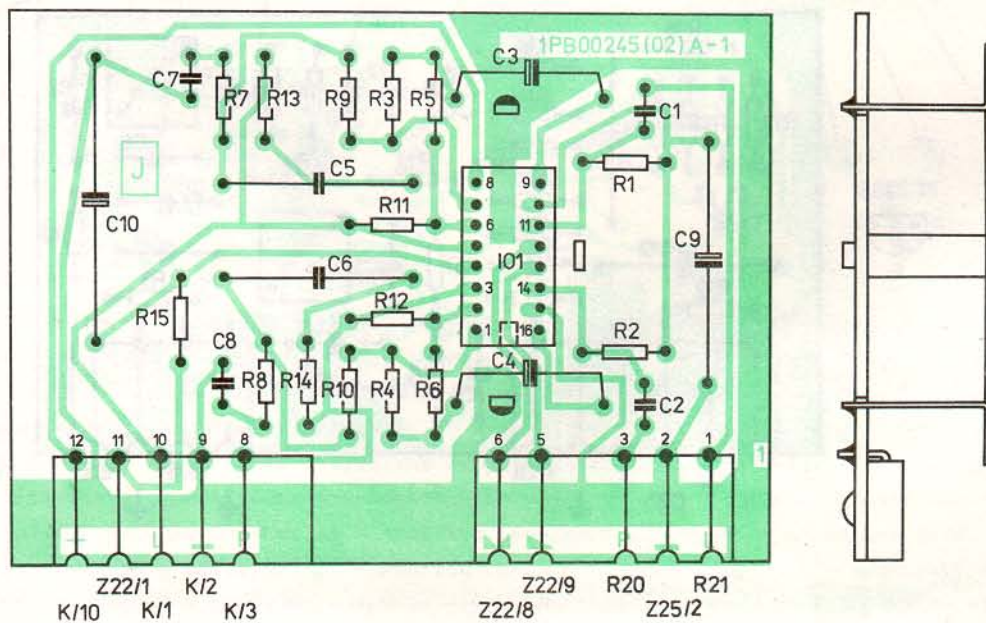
Montážní zapojení stereofonního dekodéru (E)
